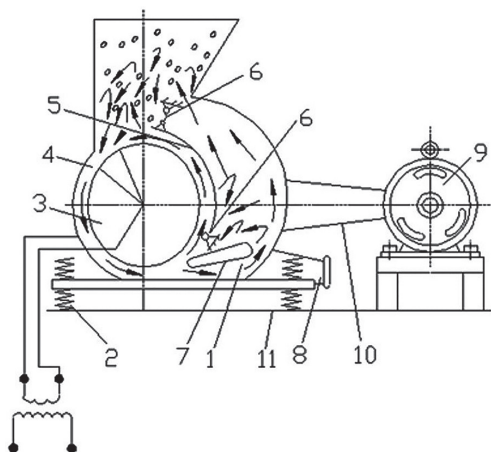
Дезинтегратор: 1 – корпус; 2 – упругие опоры; 3 – ротор; 4 – дебаланс; 5 – откидной щиток; 6 – шарниры; 7 – рассекатель; 8 – разгрузочное устройство; 9 – электродвигатель; 10 – клиноременная передача; 11 – станина
